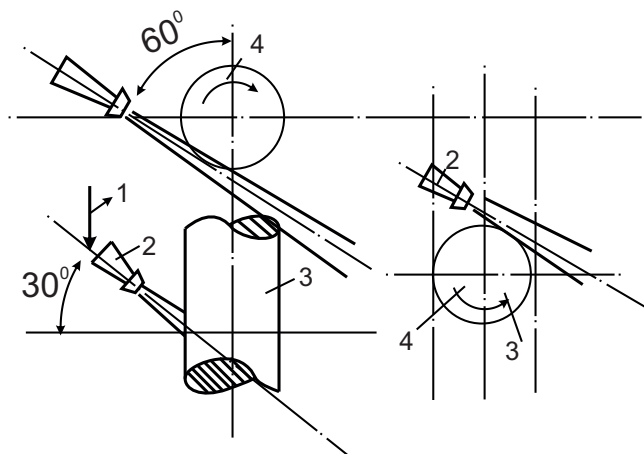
Схема расположения плазменной горелки относительно вращающейся детали:
